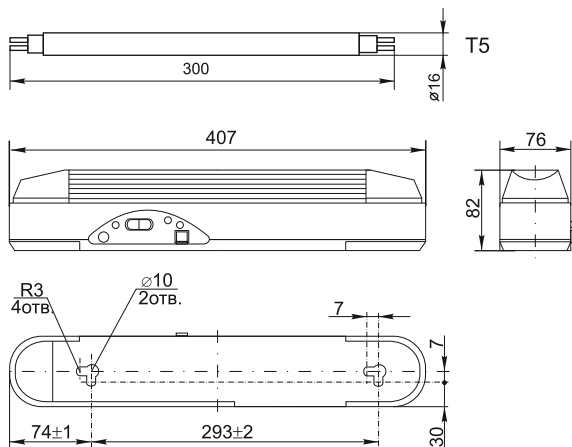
Габаритные размеры светильников ЛБА 3923, ЛБА 3923А
